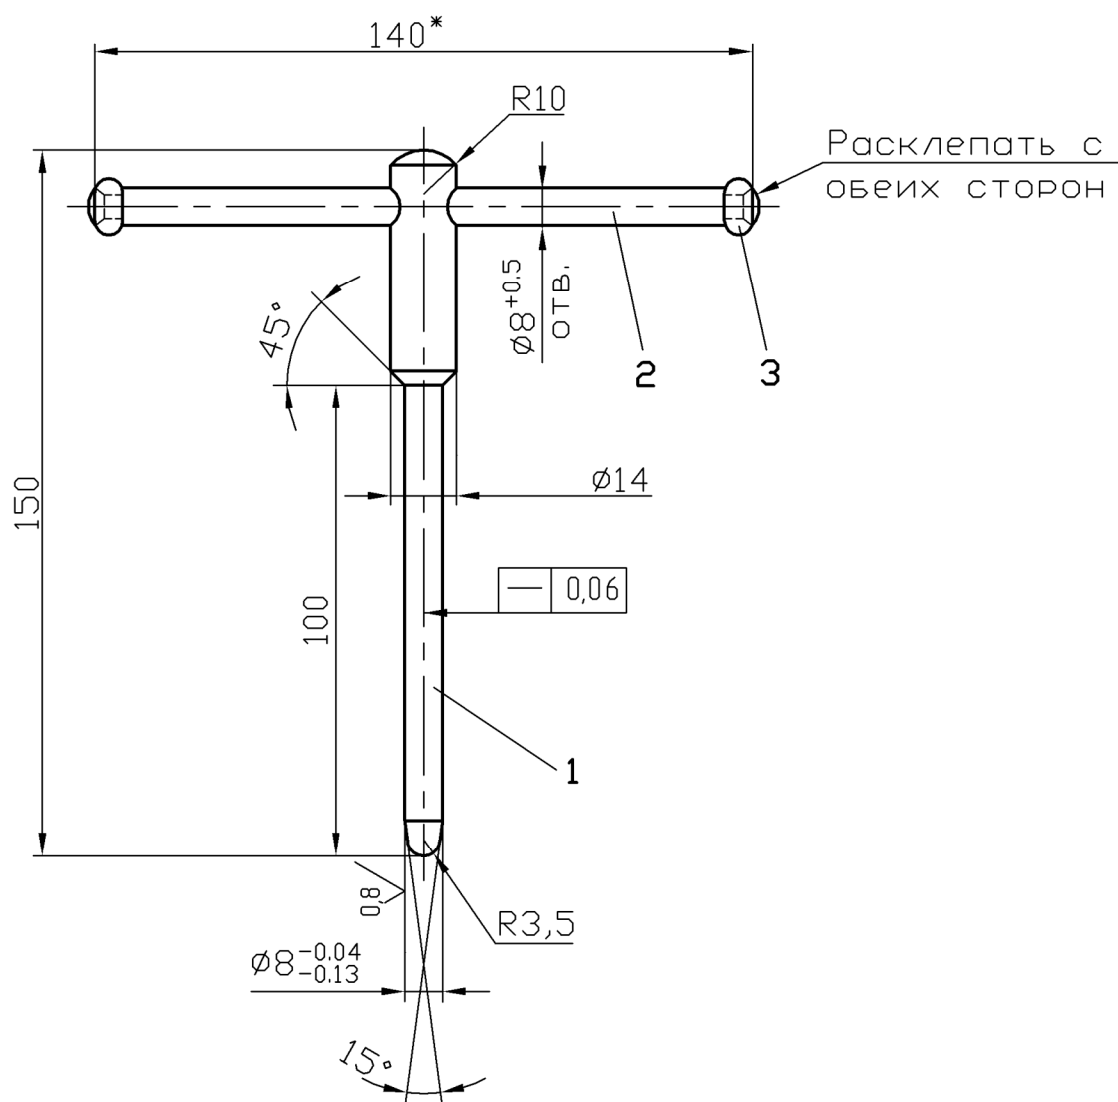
Штифт установочный коленчатого вала 3М 7820-4582:
